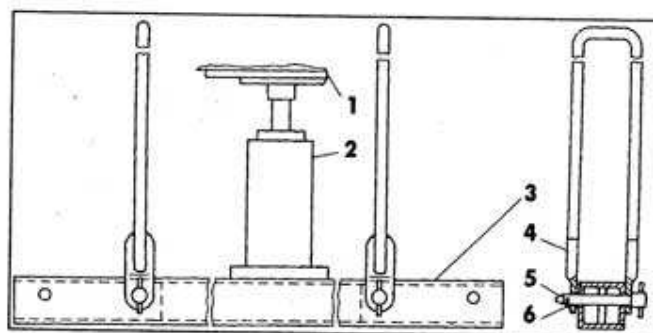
Приспособление 7879–4518 для установки рессор:
